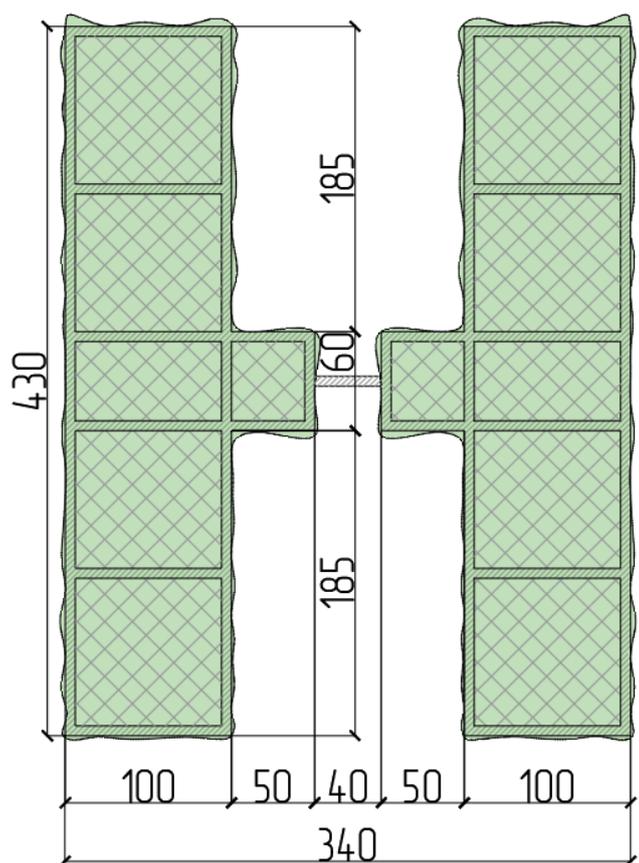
Фронтальный вид. Схема сборки буквы Н. Надпись ДИНОПАРК.
